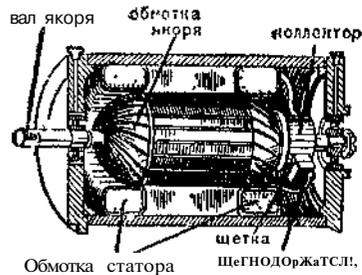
Коллекторный двигатель для бытовых м.ш.ш.п.
